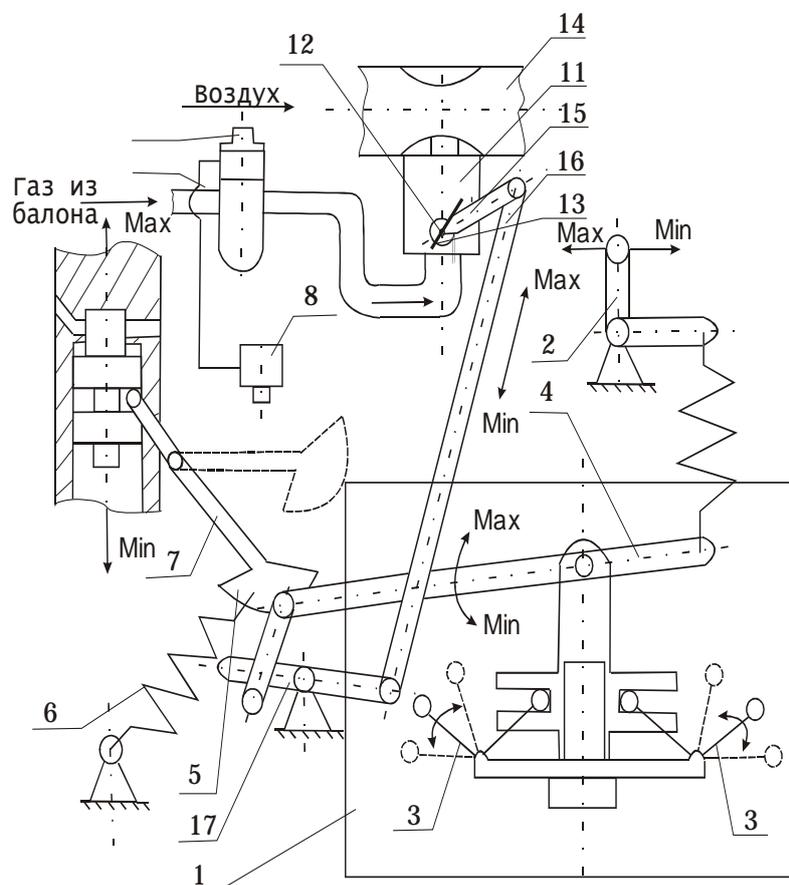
Система регулирования газообразного (испаренного) топлива: 1 – центро-бежная муфта; 2 – рычаг управления регулятором; 3 – грузы; 4 – главный (основной) рычаг; 5 – сектор; 6 – пружина сектора; 7 – двулучий рычаг; 8,9 – органы переключения режимов работы дизеля; 10 – проводник; 11 – дозатор; 12 – спиральная пружина; 13 – заслонка; 14 – смеситель; 15 – рычаг заслонки; 16 – тяга; 17 – двулучий рычаг
